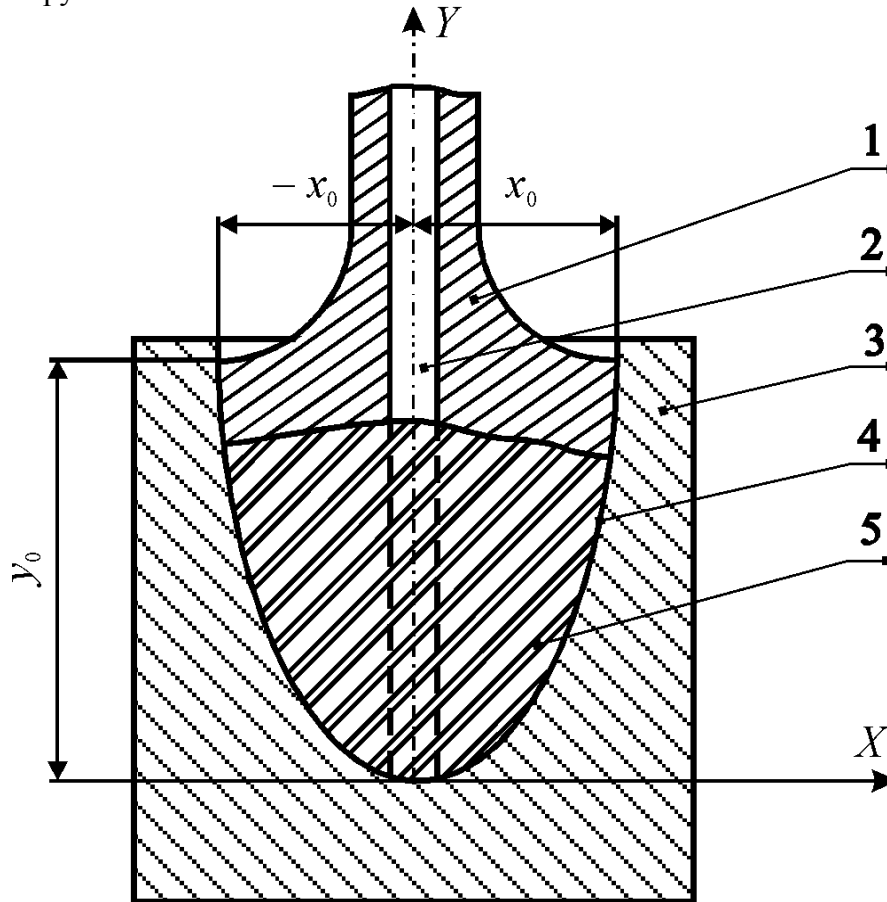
Упорний гідростатичний підшипник з параболічними робочими поверхнями
